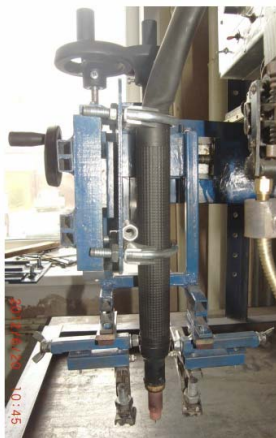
Внешний вид сварочной головки с двухплечевым разделённым токоподводом
